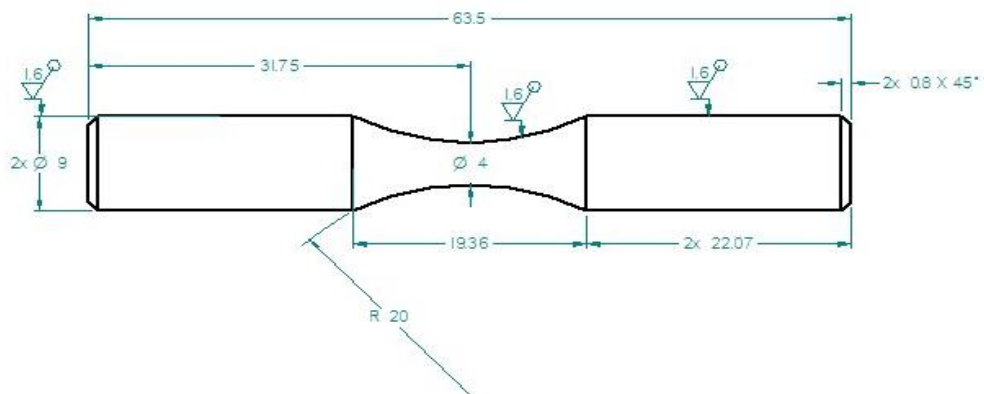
Dimensiones geométricas de probeta para fallo a fatiga.
